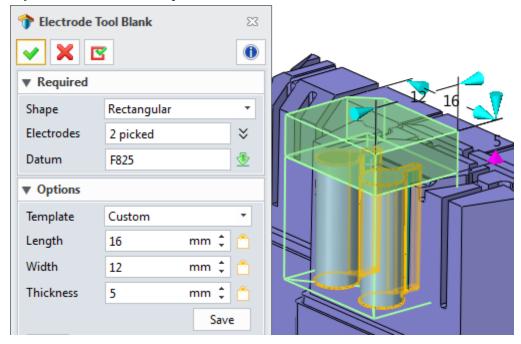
Dimensión básica para el blank del grupo de electrodos 2
